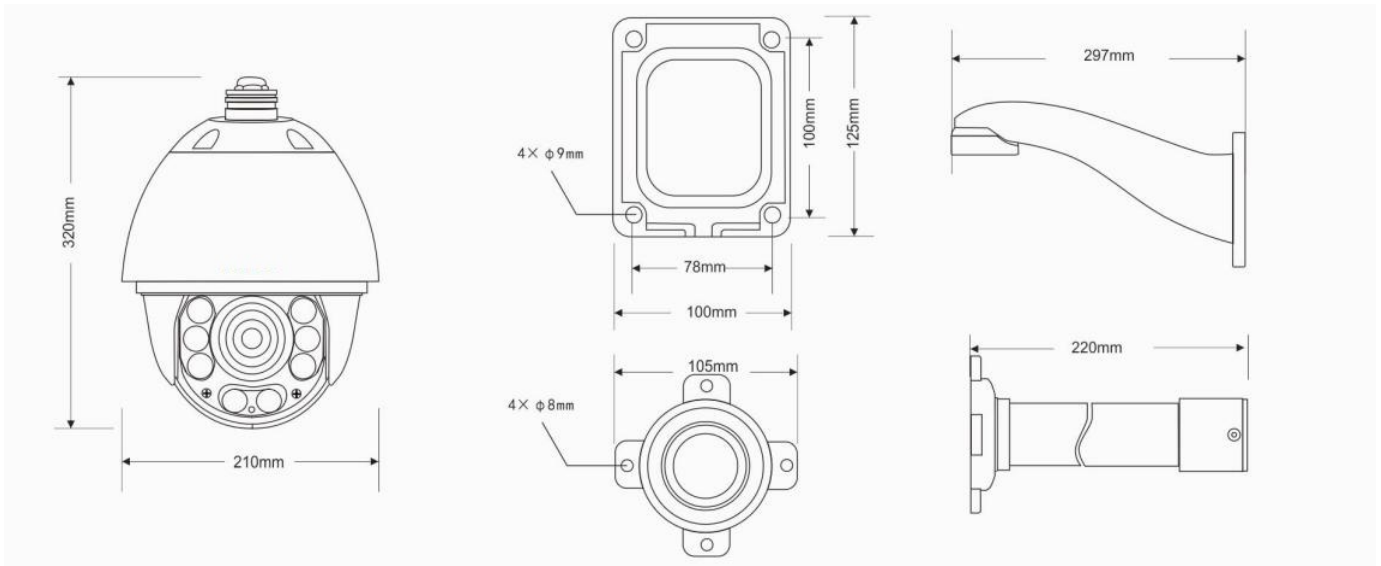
Габаритный чертеж видеокамеры ИВМС-601.
